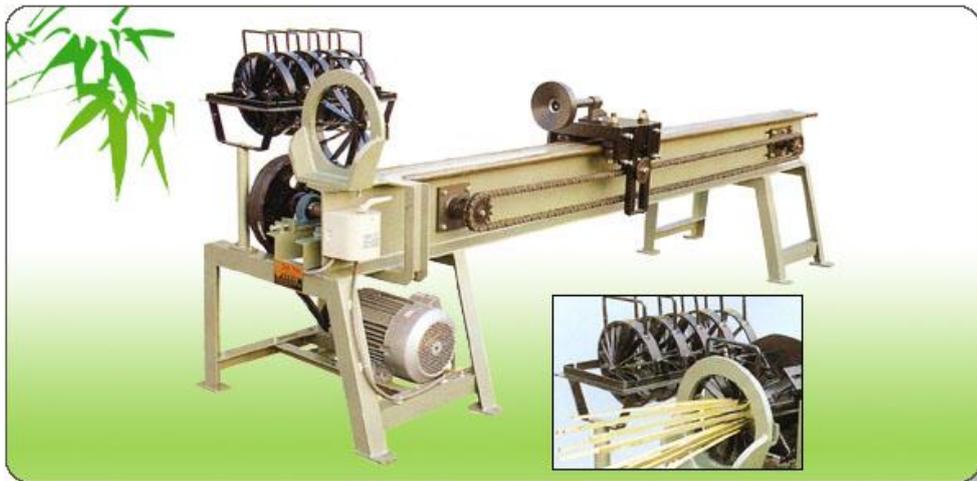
Corte longitudinal do bambu, uso de faca tipo estrela.
